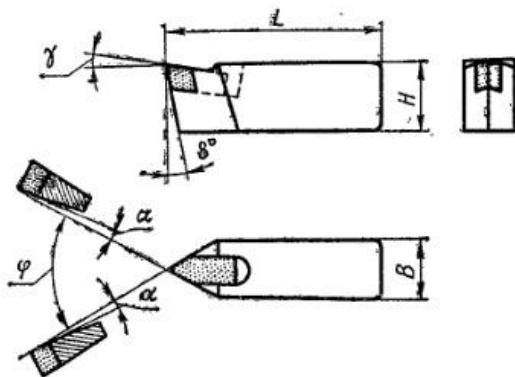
Резьбовой резец для нарезания резьбы вихревым способом:
